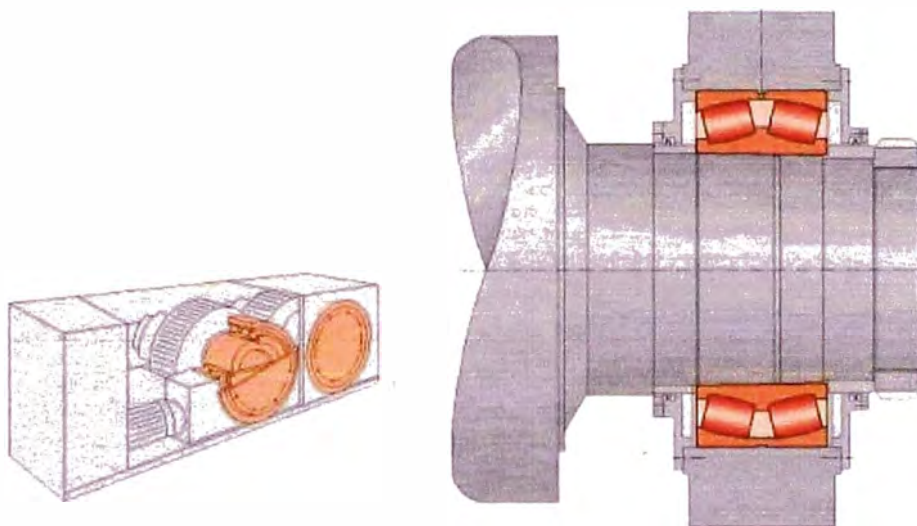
Rodamiento de rodillos esféricos en chancadora rodillos-prensa.
